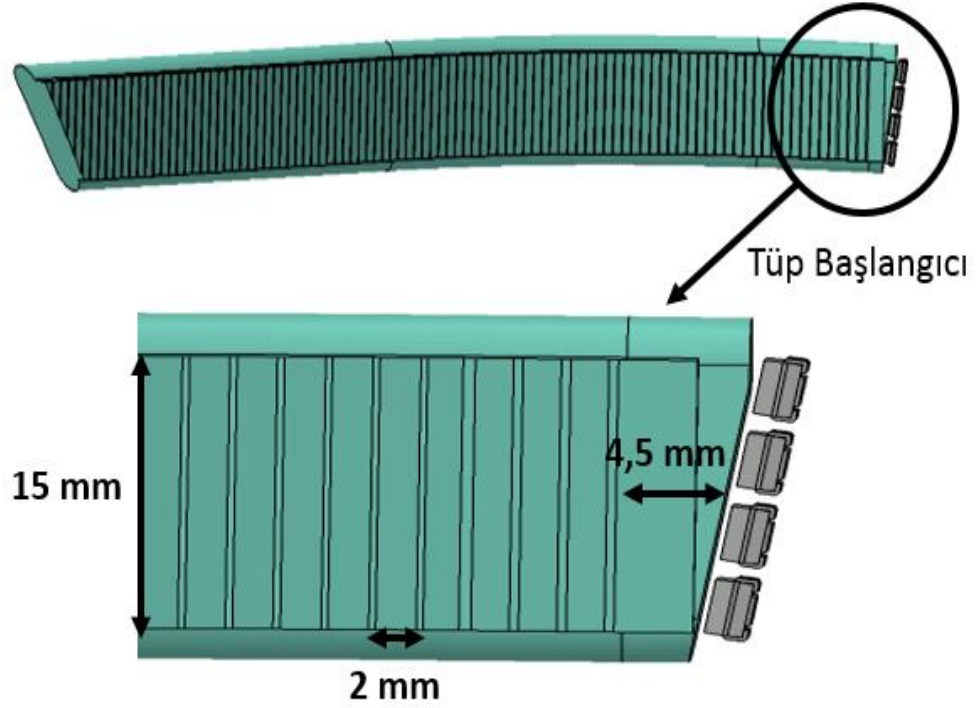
LED' lerin PCB üzerindeki konumları ve aralarındaki mesafe
